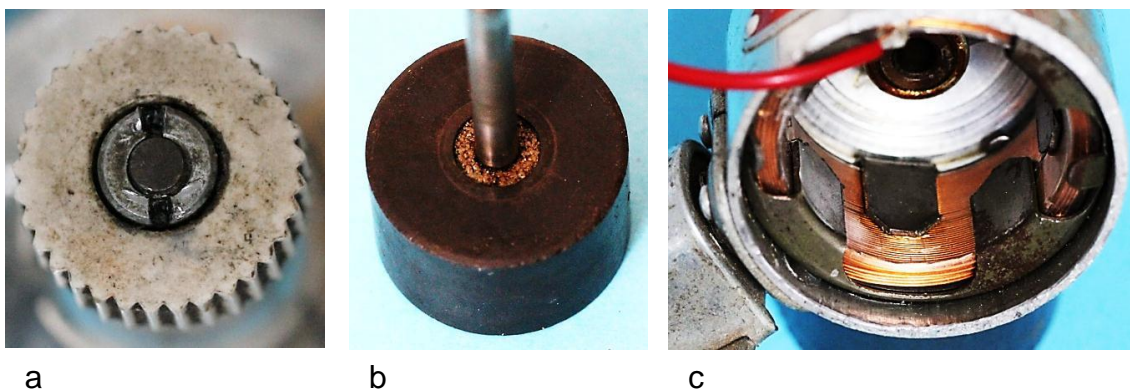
Generator: a) Specksteinreibrad mit versenkter Schlitzmutter, b) Polrad (30 mm Durchmesser, 18 mm axiale Länge), c) Klauenpolanker
